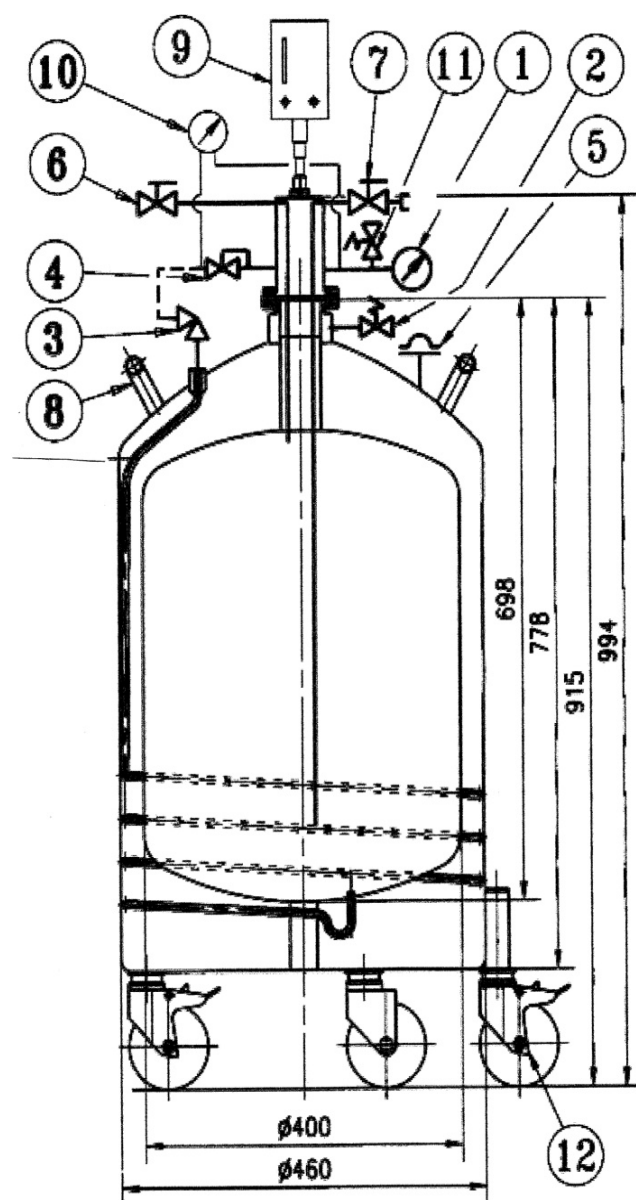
Принципиальная схема резервуара XRP 60 S. (1 – манометр; 2 – разгрузочно-предохранительный клапан; 3 – клапан восстановления давления; 4 – стабилизатор давления; 5 – разгрузочное отверстие; 6 – спускной клапан; 7 – заправочно-сливной клапан; 8 – ручки; 9 – емкостный уровнемер; 10 – измеритель уровня жидкости перепада давления; 11 – разгрузочная головка вентильная; 12 – 5 роликов Ø100 (3 поворотных + 2 запорных)).
